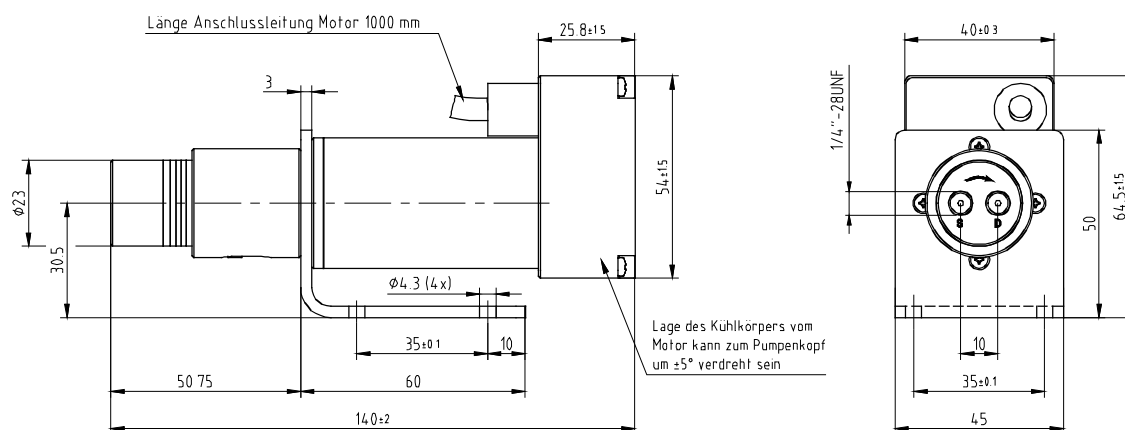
Abmessungen Mikrozahnringspumpe mzzr-2505
